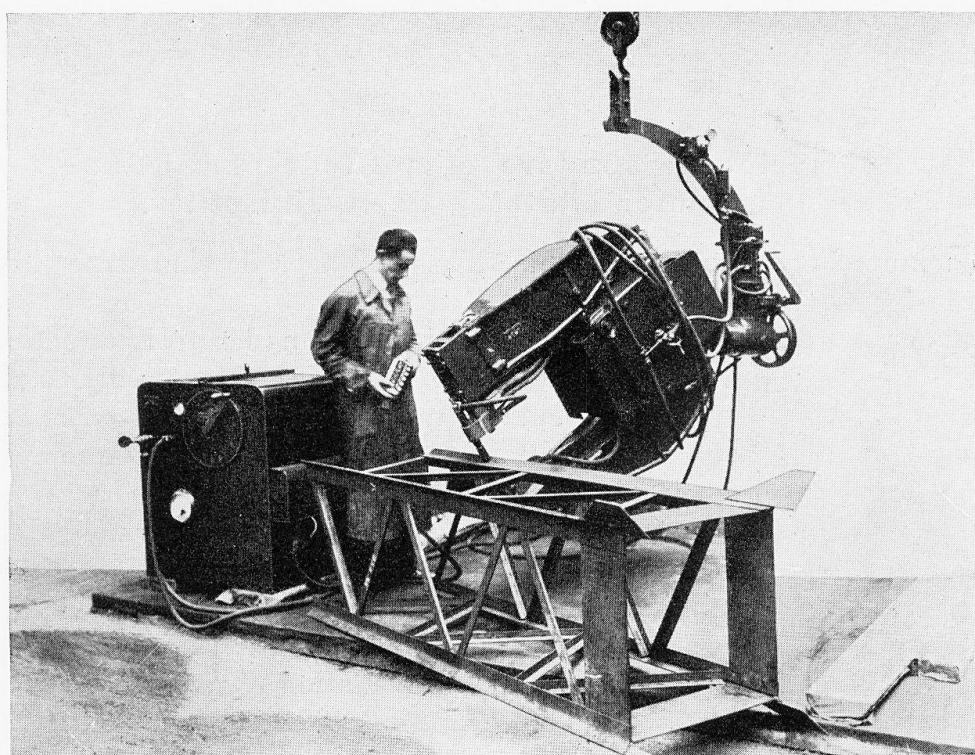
Machine inclinée soudant un pylône = Geneigte Maschine beim Schweißen eines Mastes = Machine inclined, welding a pylon.
